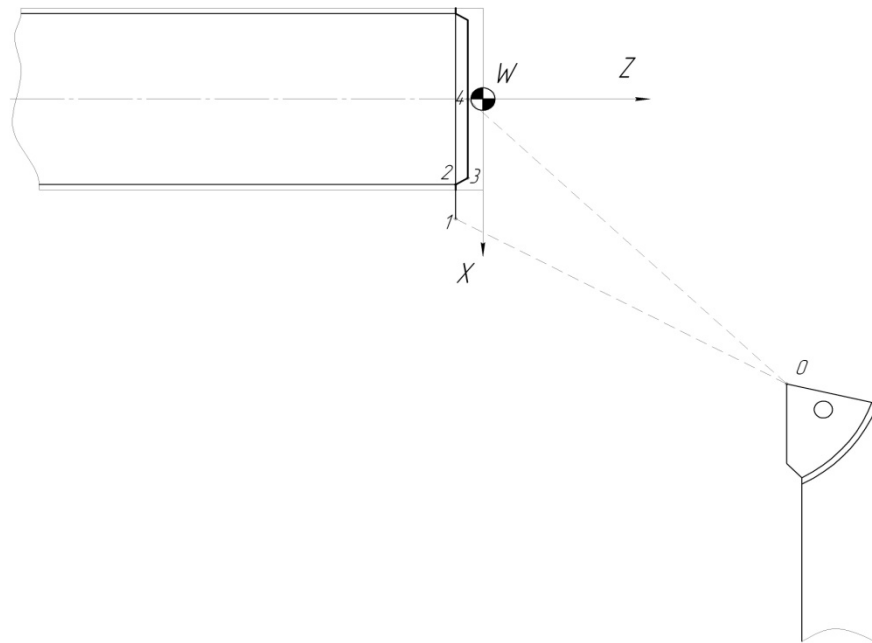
Система координат токарного верстата з ЧПК мод. 16К20Ф3
